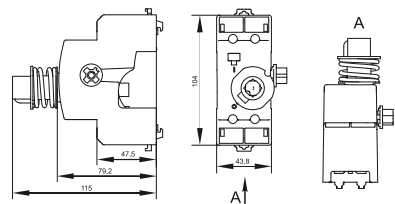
Габаритные размеры модуля взвода / Figure 1 – Overall dimensions of operating module
